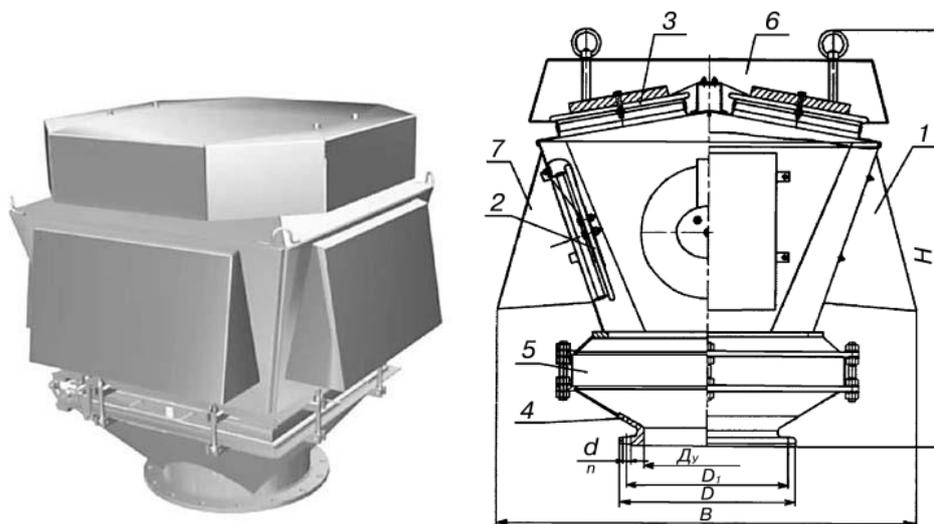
Дыхательный клапан КДС 1500/200. Изображение (слева) и общий вид (справа), [163]: 1 – корпус; 2 – тарелка вакуума; 3 – тарелка давления; 4 – переходник; 5 – кассета огневого предохранителя; 6 – крышка; 7 – воздуховод
